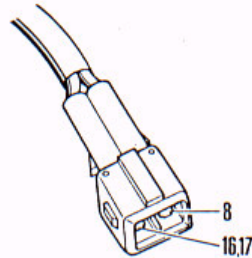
Vyhřívání podložka (sv. 3 viz také obr. 59; A - od relé vyhřívání podložky)
